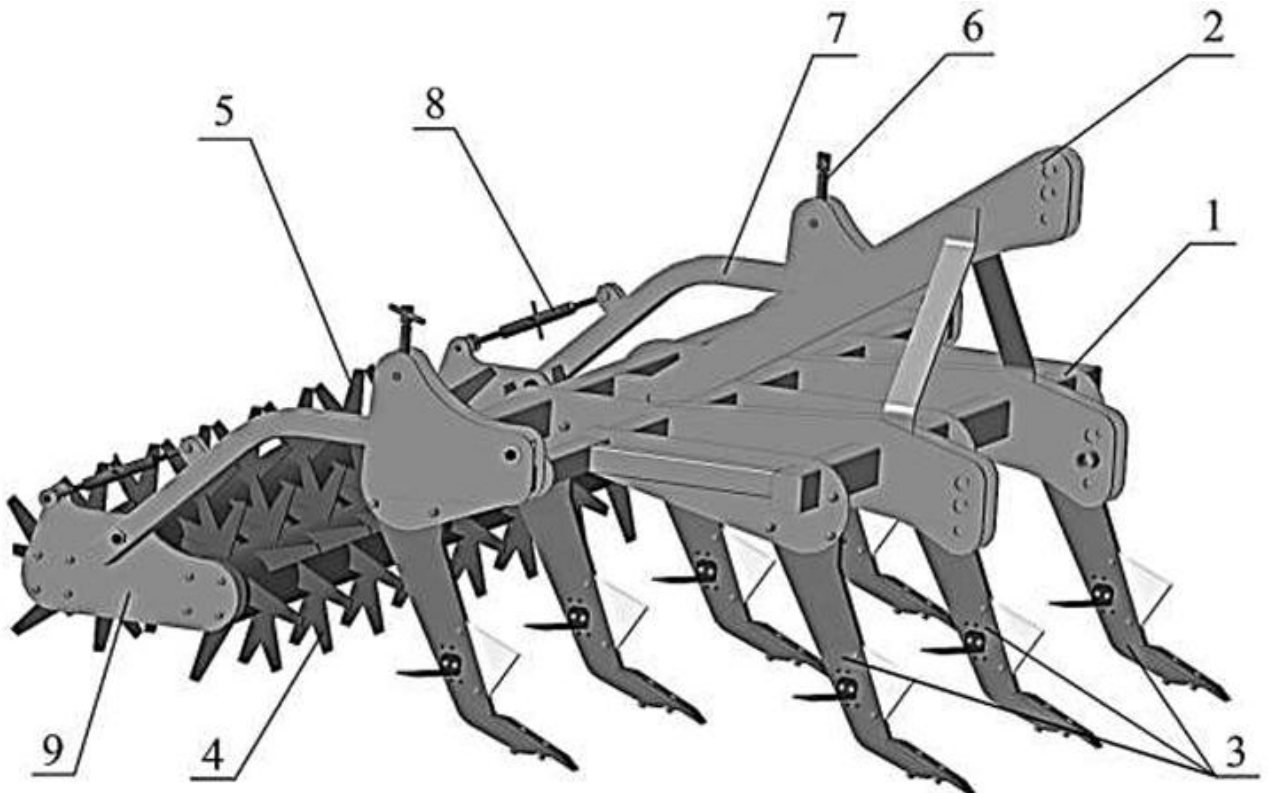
Схема та загальний вигляд комбінованого чизеля ЧН: 1 – рама; 2 – верхня ланка начіпного пристрою; 3 – чизельна лапа; 4 – зубчастий коток передній; 5 – зубчастий коток задній; 6 – гвинтовий механізм регулювання глибини обробітку ґрунту; 7 – кронштейни навішування котків на раму чизеля; 8 – гвинтова тяга регулювання положення котків; 9 – бокова пластина кріплення котків
